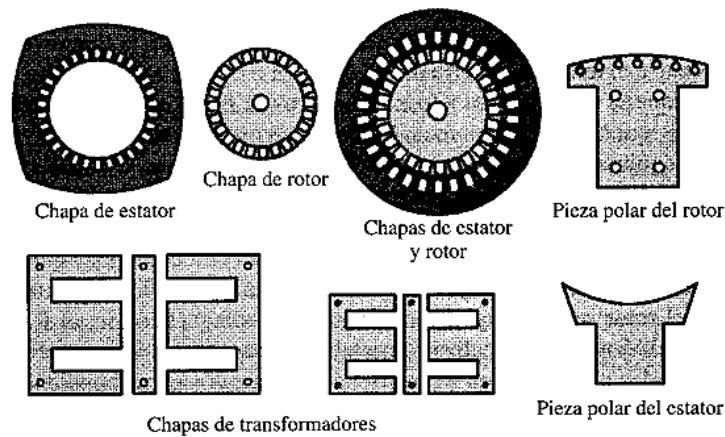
Tipos de Chapas magnéticas - Máquinas eléctricas Jesús Fraile Mora quinta edición [3].
